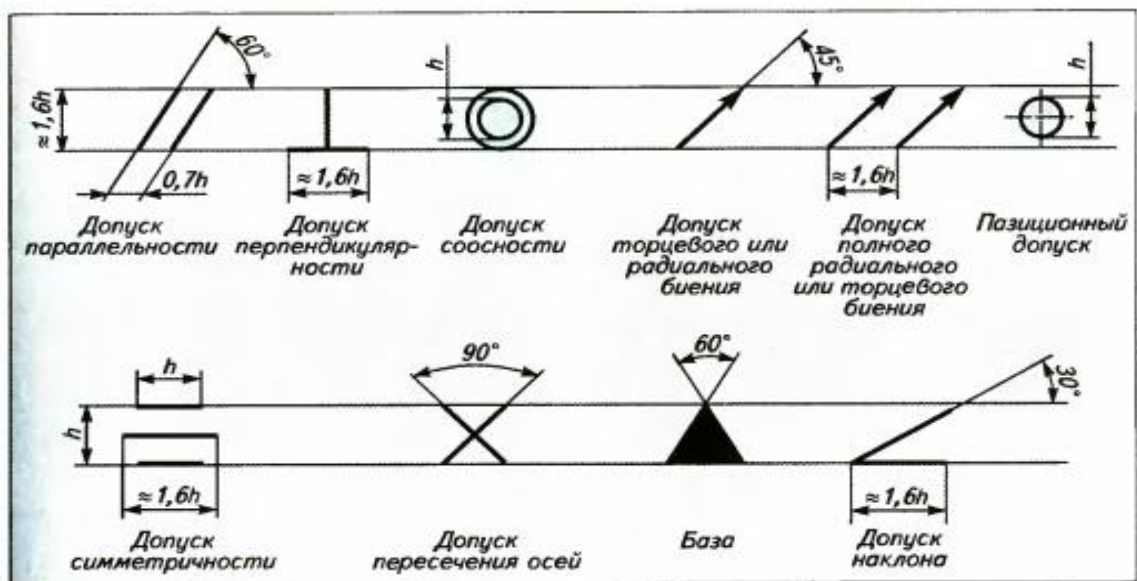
Формы и размеры знаков для обозначения допусков
